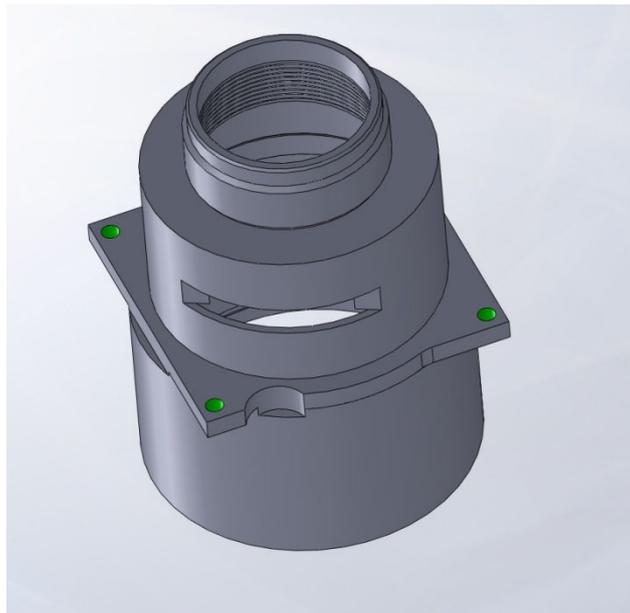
Трехмерный эскиз для сверлильной операции с визуальным изображением обрабатываемых отверстий
